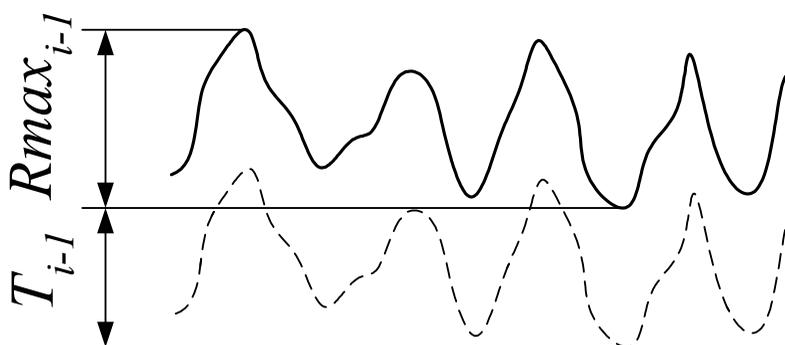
Схема поверхностного слоя материала поверхности заготовки
